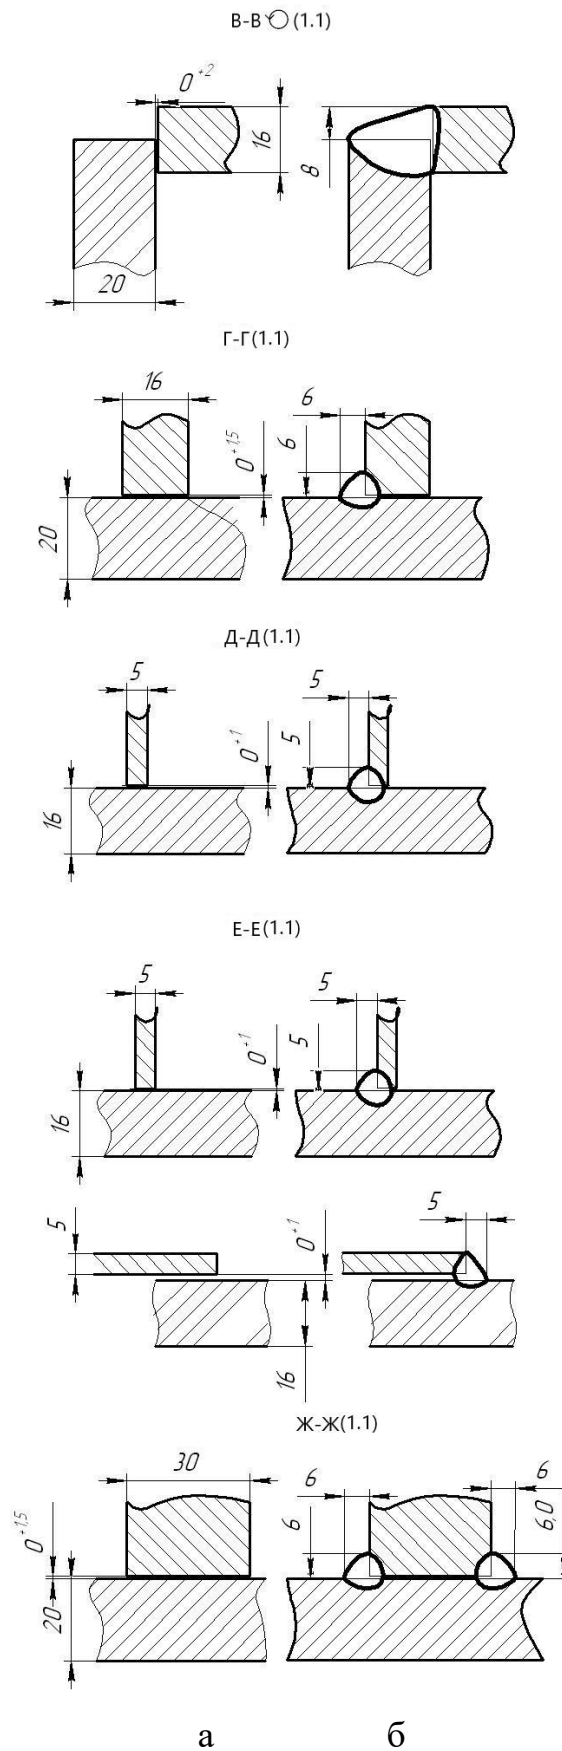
Розріз кромки (а) і готового зварного шву (б) у відповідності з ГОСТ 14771-76 (див. креслення НУЗП 000023.001 СК)
